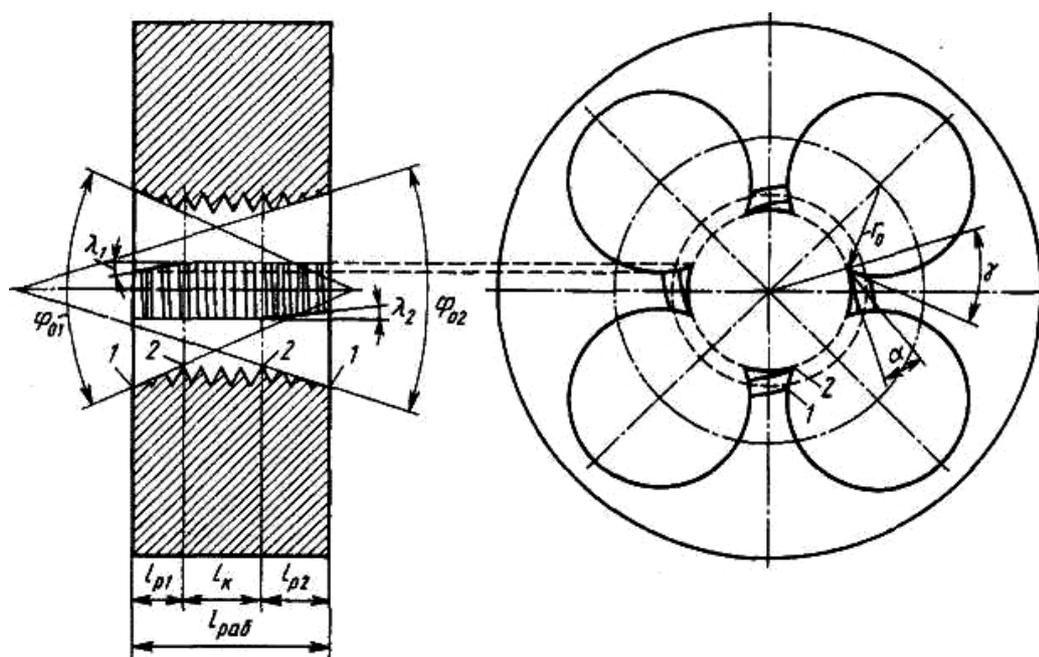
Круглая плашка для нарезания наружной резьбы на стержнях
